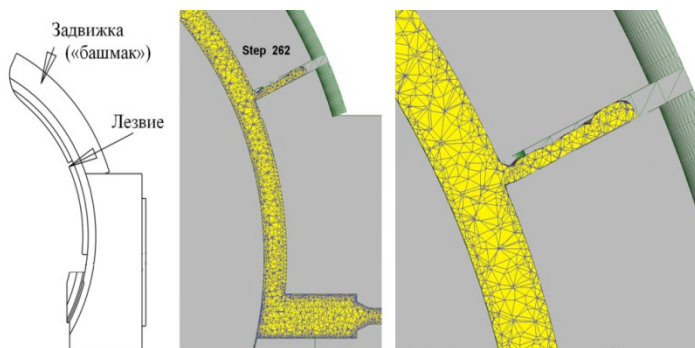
Матричный узел с лезвием для снятия облоя с контакта «заготовка – башмак»
